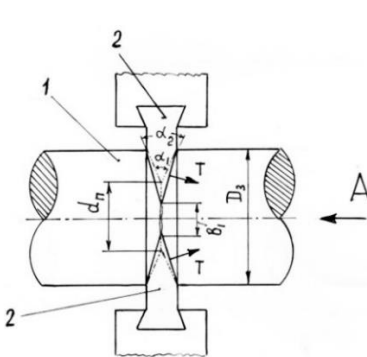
Друга стадія розподілу гарячої заготовки прямими бойками: 1 – заготовка; 2 – бойок.
